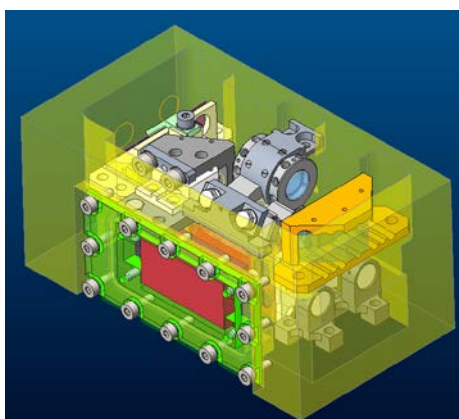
3D модель варианта компоновки излучателя лазерного дальномера
